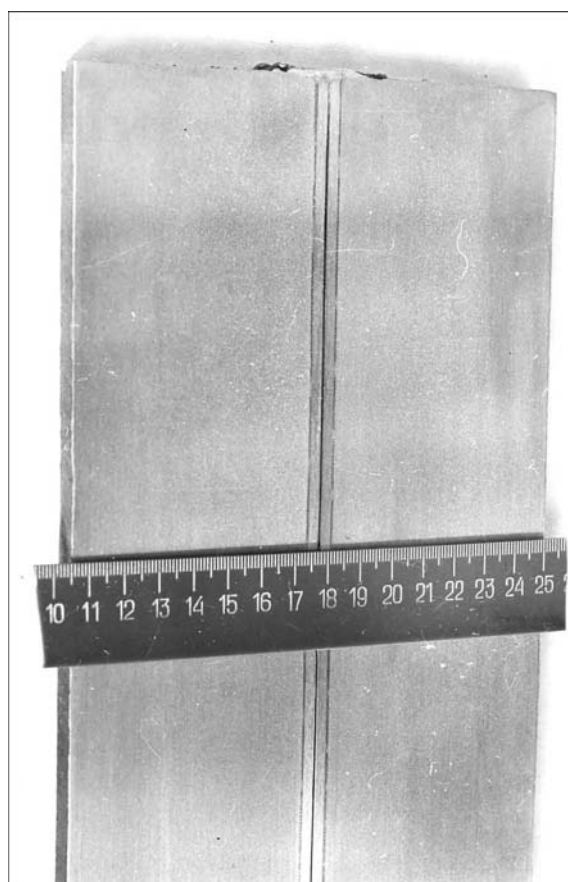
Макрошлиф толстолистового биметалла, полученного способом АВП симметричного пакета
